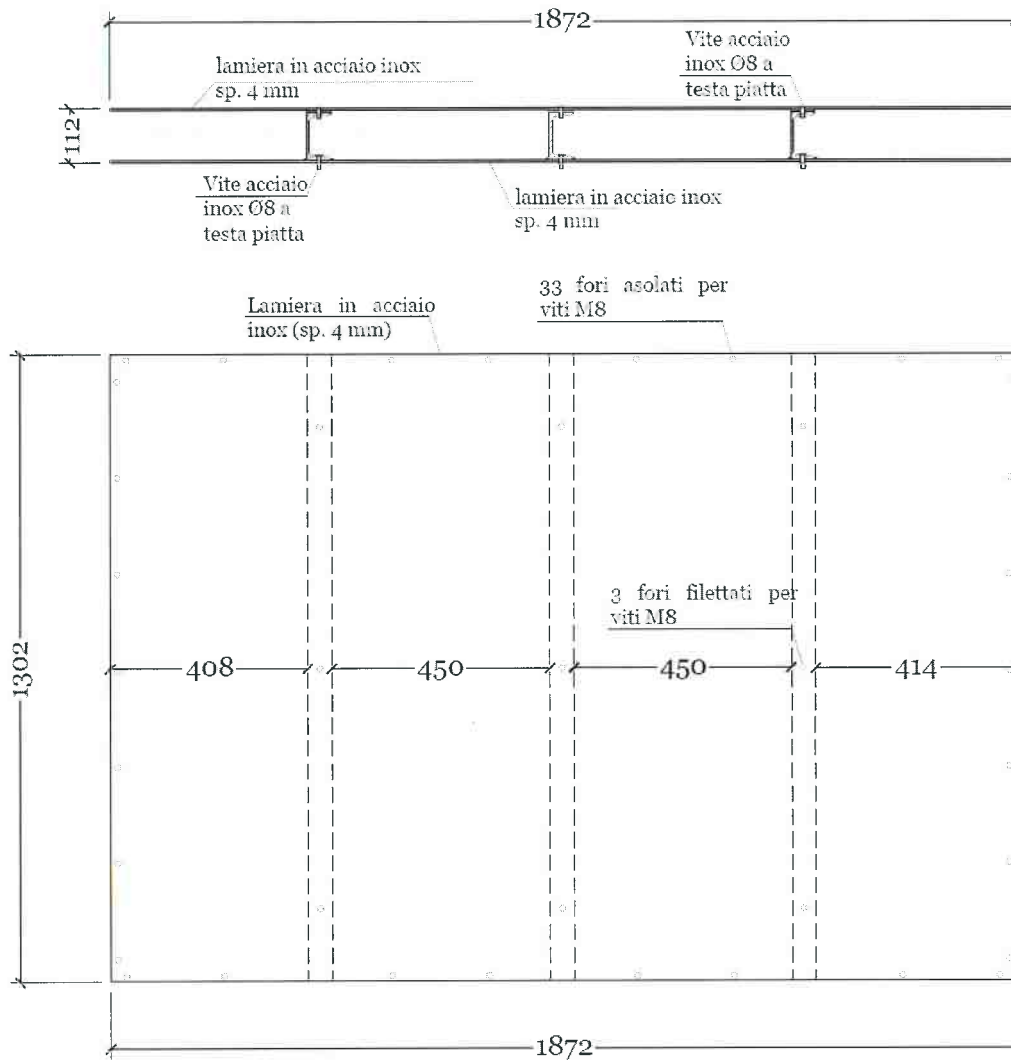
Vista in pianta e prospetto dell'elemento costruttivo: pannello sandwich
